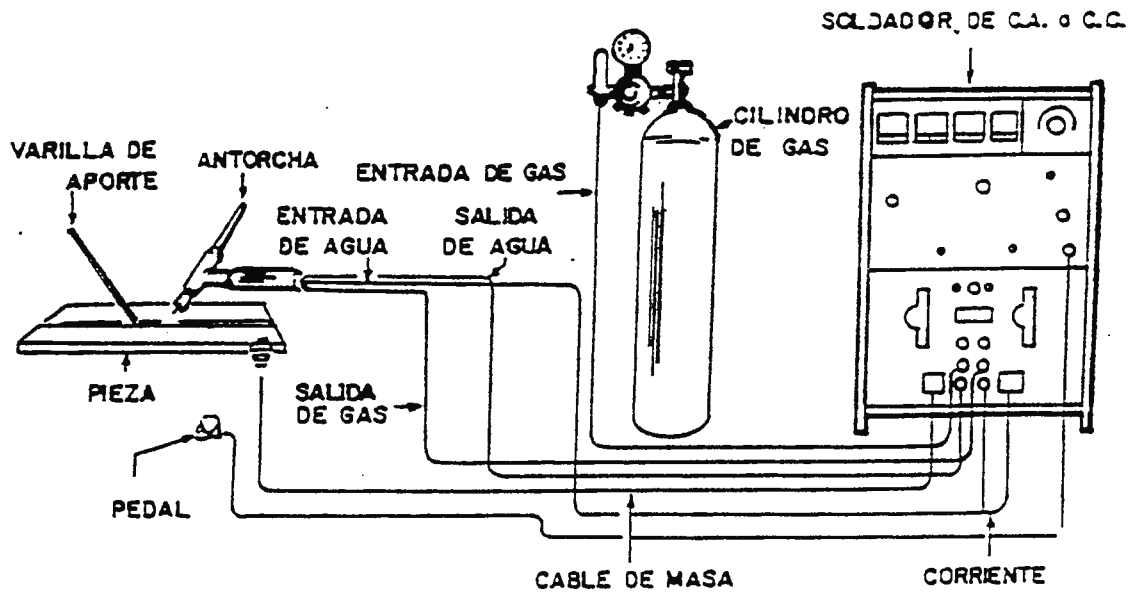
Equipo de soldadura T.I.G.
